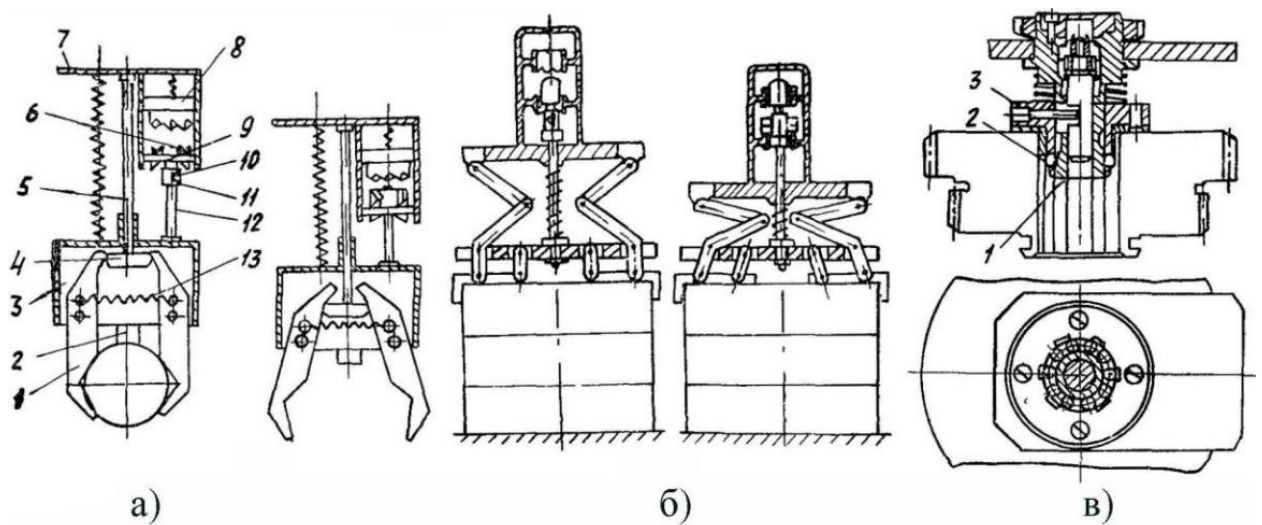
Схемы устройств для захватывания валов или фланцев за наружную поверхность
